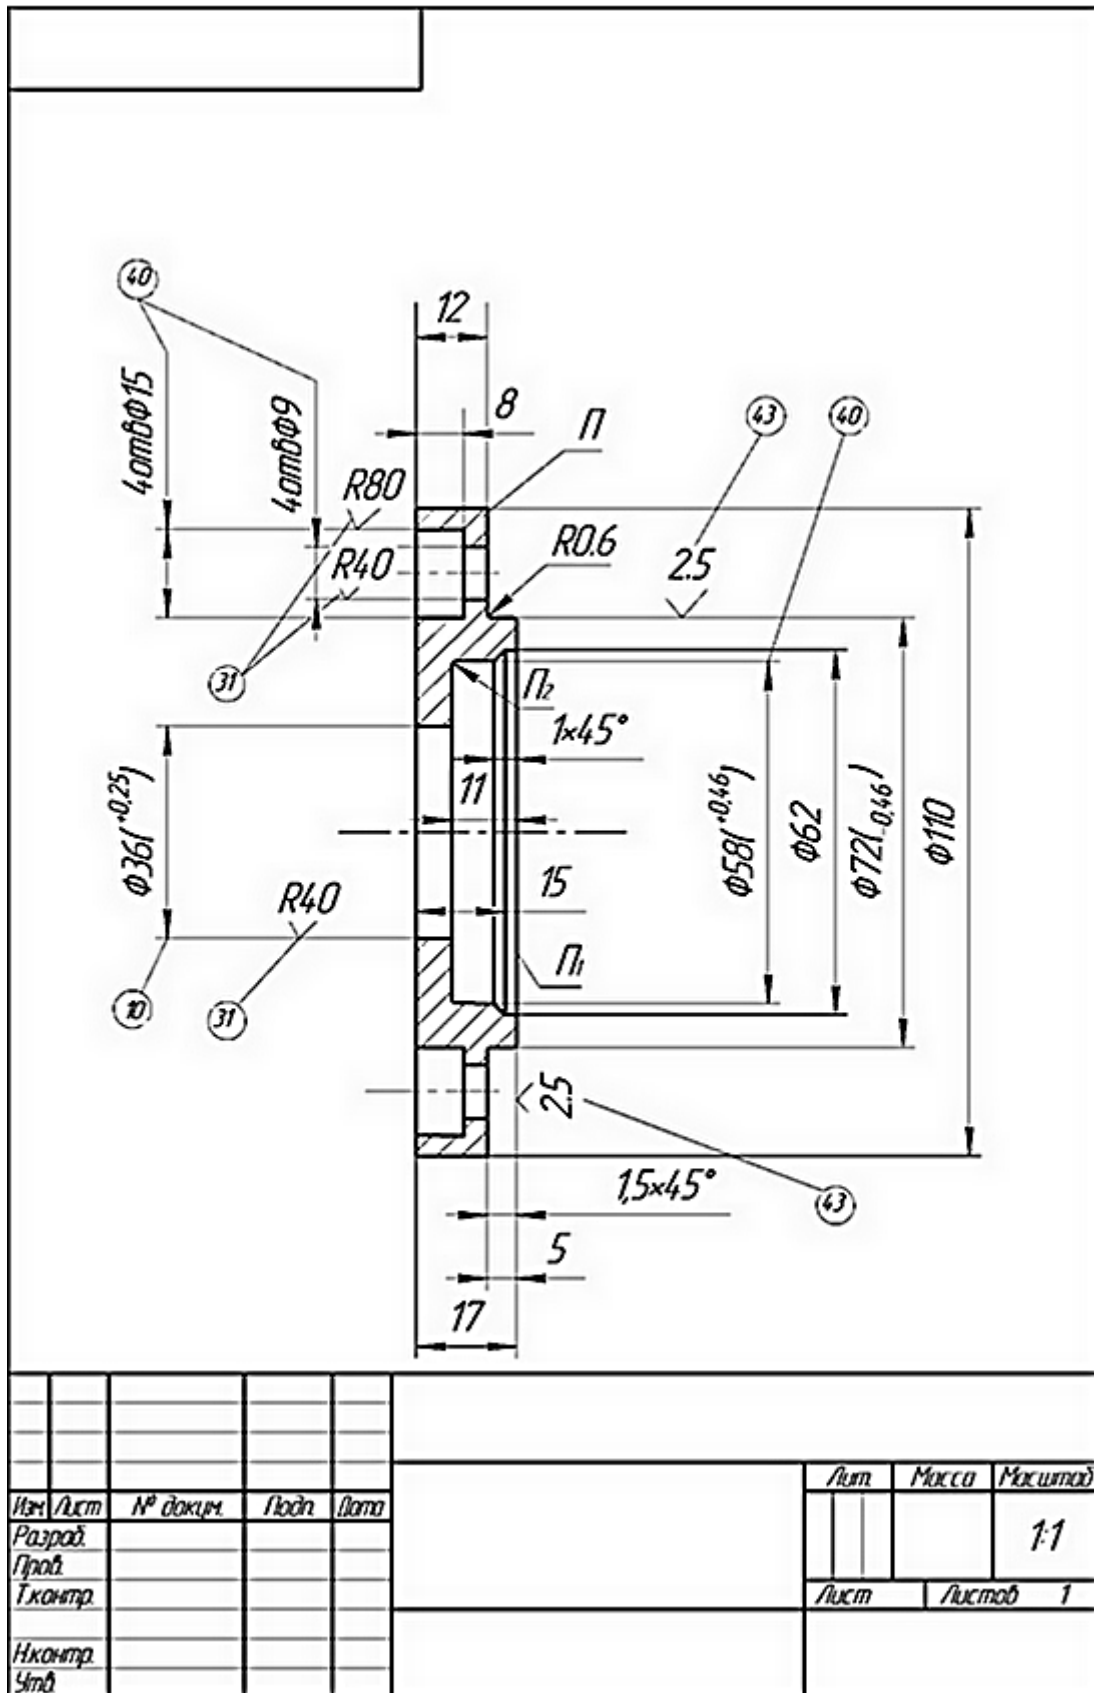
Рабочий чертеж крышки подшипника (с ошибками)
